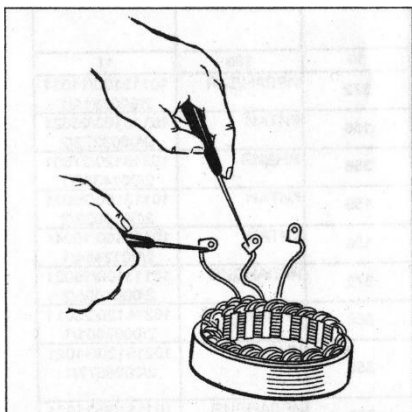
Проверка обмотки выключателя на обрыв
